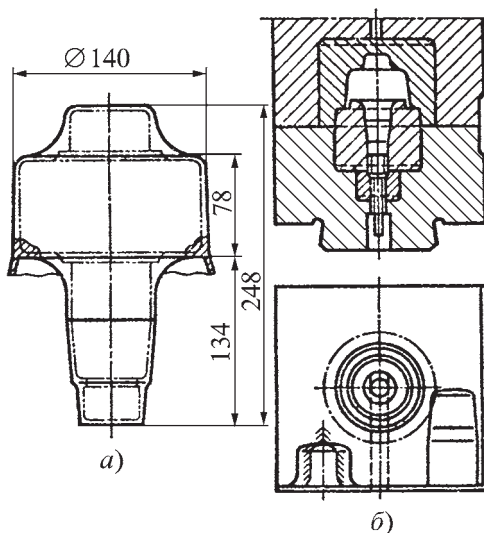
Поковка с длинным стержнем (а) и штамп с двумя заготовительными ручьями (б); в окончательном ручье применен выталкиватель
